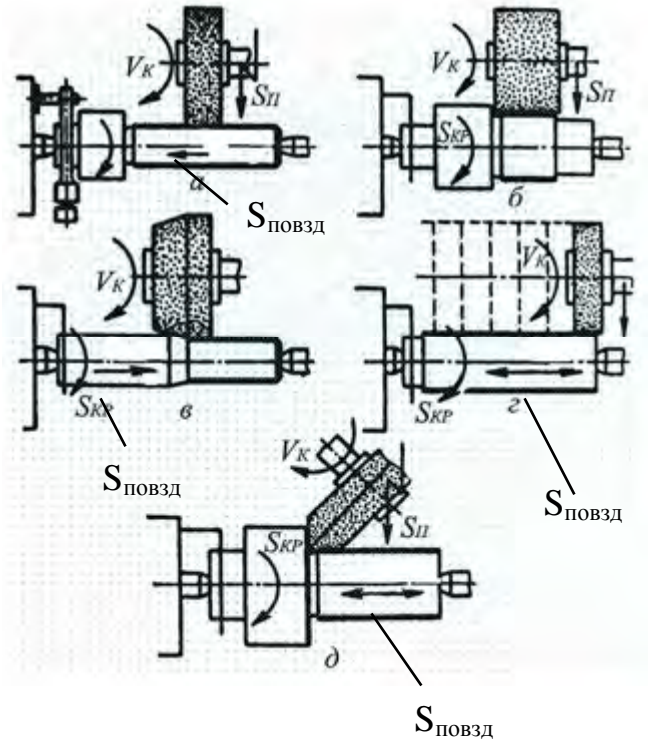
Схеми оброблення заготовок на круглошліфувальних верстатах
